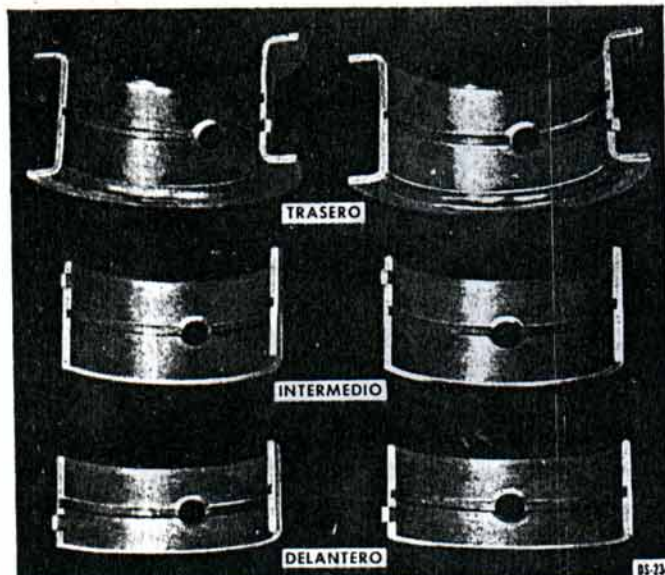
Conjunto cojinetes de bancada para motores 4L-151.
